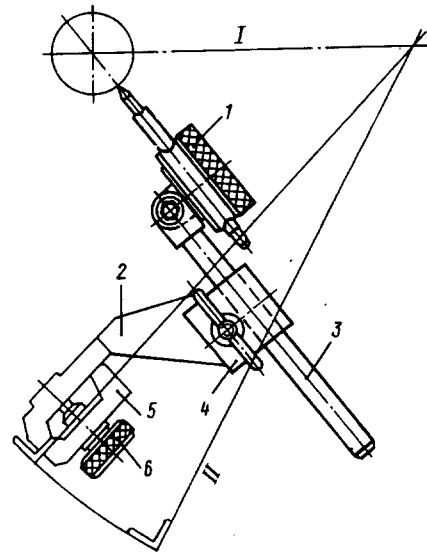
Приспособление для проверки биения вала трансмиссии:
